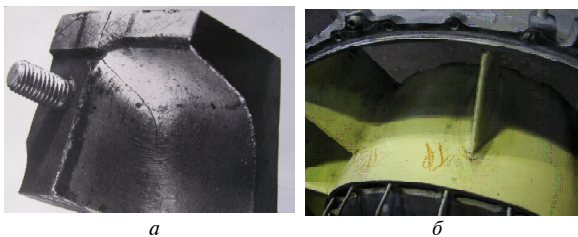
Трещины на поверхности отливок из сплава Мл-10,  $\times 0,1$ : а – фрагмент лобового картера, б – корпусная деталь
